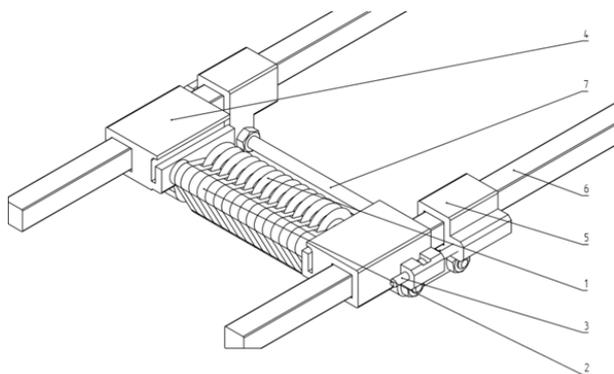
Механизм вертикального реза для мягких пород древесины:
